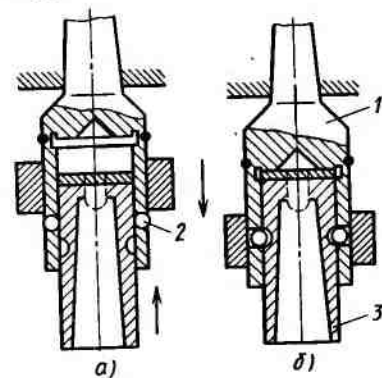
Быстросменный патрон для зажима сверл, зенкеров и разверток
